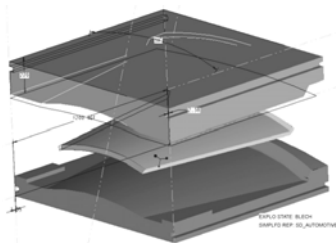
Схема прессования заготовки в сегмент. Заготовка расположена внутри формообразующих стальных вставок штампа [26]
